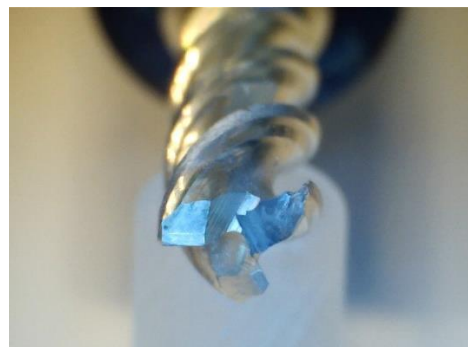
Detailaufnahme "verschlissenes" Werkzeug
